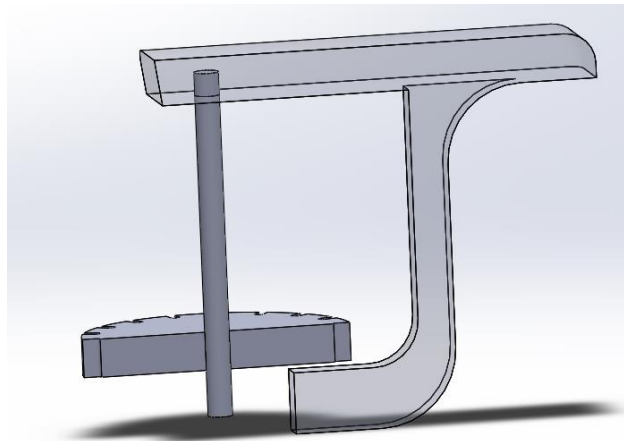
Vista frontal de la unión a presión de componentes. Fuente: Propia.
